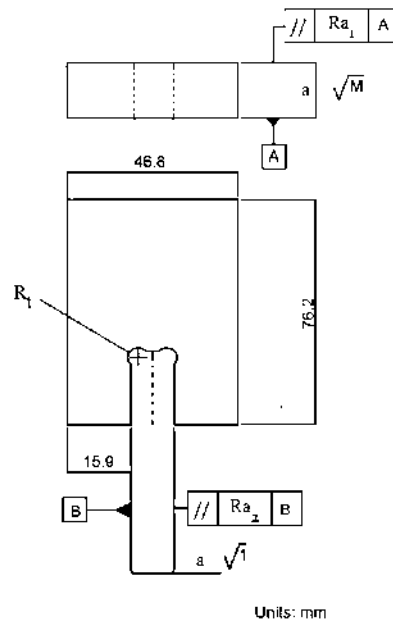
Plano de las dimensiones de probetas para el ensamble suave
